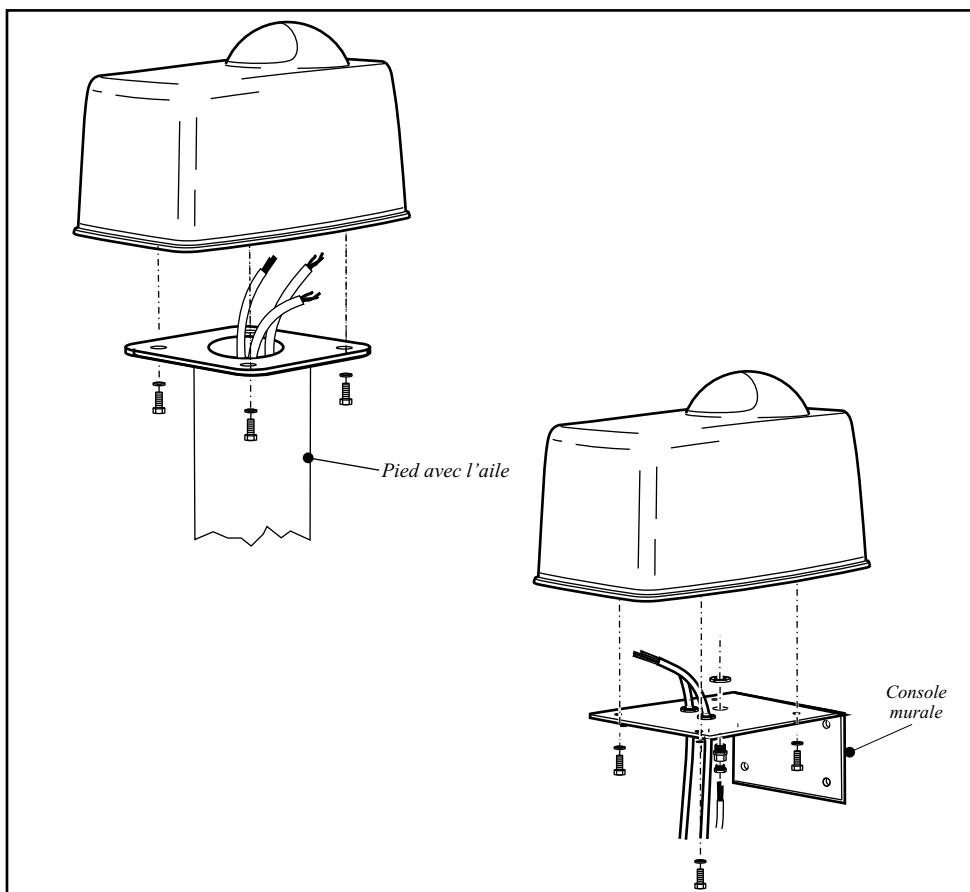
Fixez la boîte d'engrenage au pied ou à la console murale
